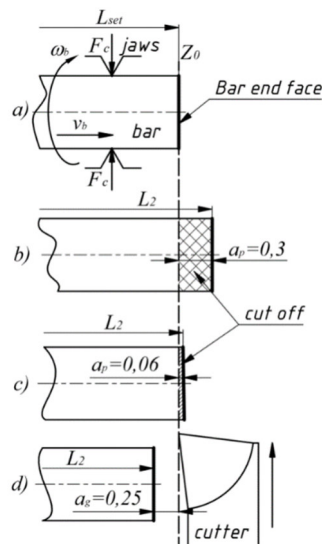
Варіанти положення торця заготовки сформованої автоматичною подачею прутка
